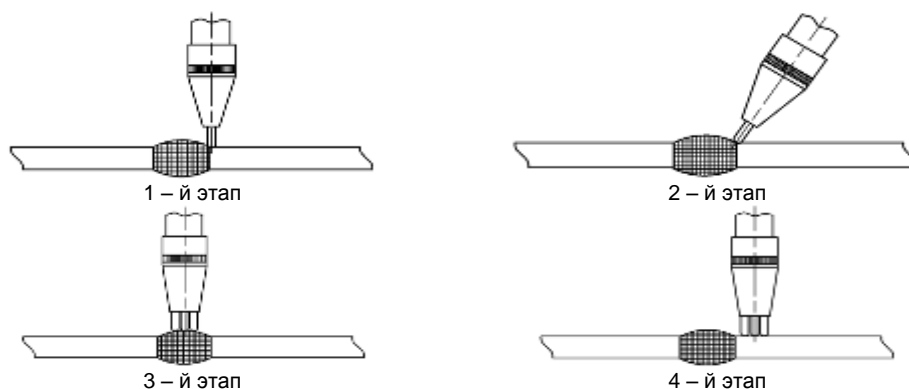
Схематический процесс обработки стыковых сварных соединений
